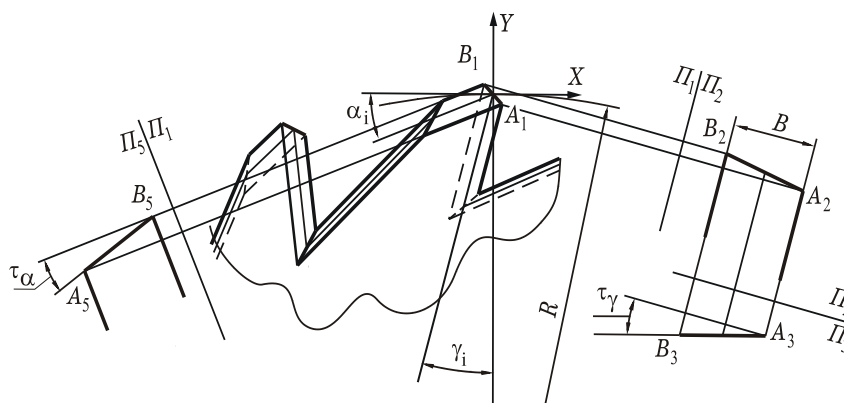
Конструктивні та інструментальні параметри зубця відрізної дискової фрези
